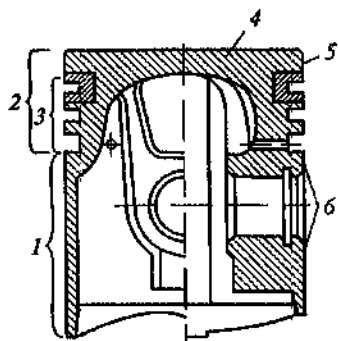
Основные элементы поршня: 1 — юбка; 2 — головка; 3 — уплотняющий пояс; 4 — днище; 5 — огневого пояса; 6 — бобышки
